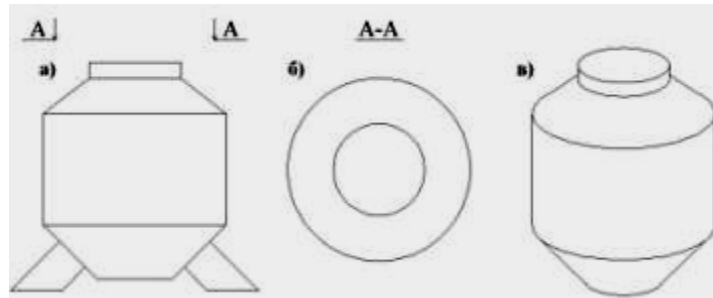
Конструктивний вигляд резервуара експериментальної біогазової установки
